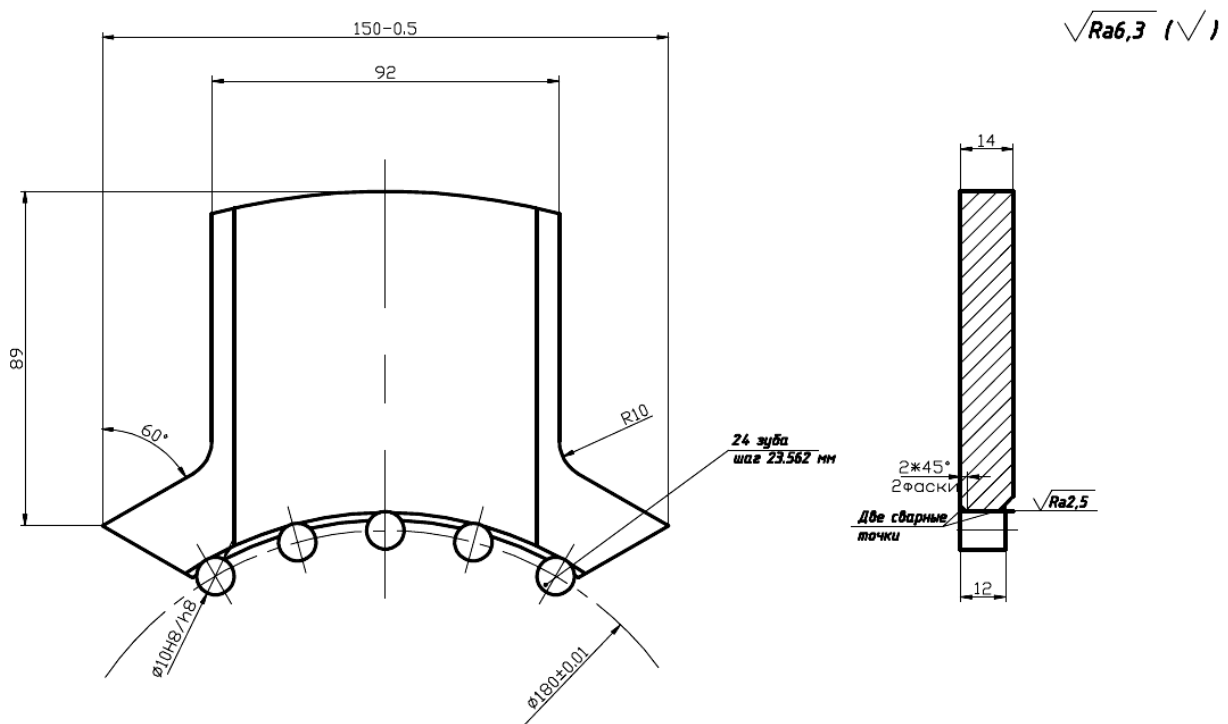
Чертеж зубчатого сектора центрального зубчатого колеса
